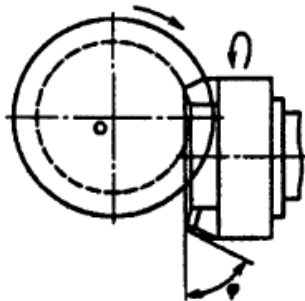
Схема фрезоточіння циліндричної деталі
